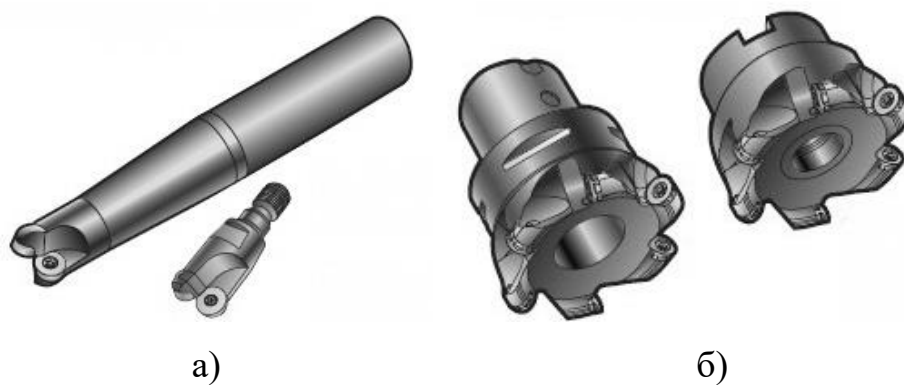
Загальний вигляд інструменту: а) з нейтральною геометрією пластини: б) з позитивною
